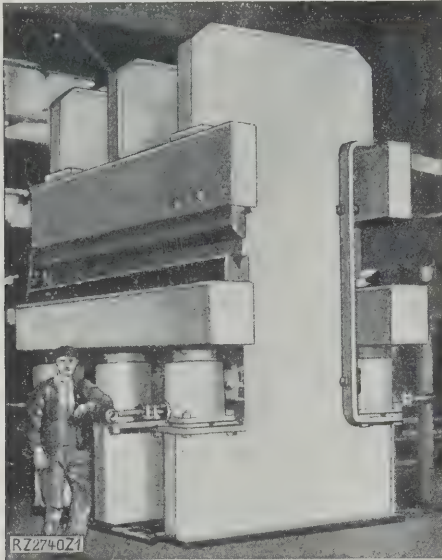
Hydraulische Presse für 1000 t Druck, ausgeführt als elektrisch geschweißte Stahlkonstruktion.
